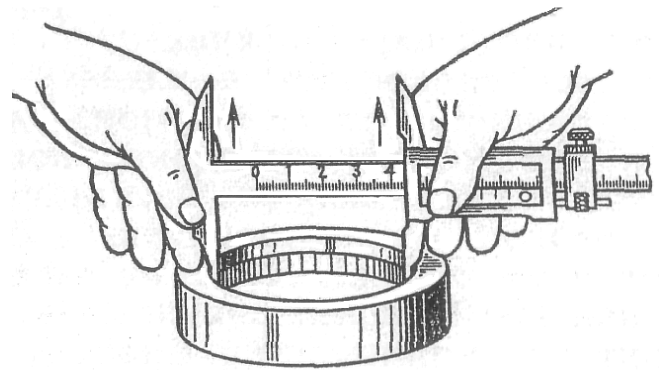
Измерение внутреннего размера штангенциркулем
